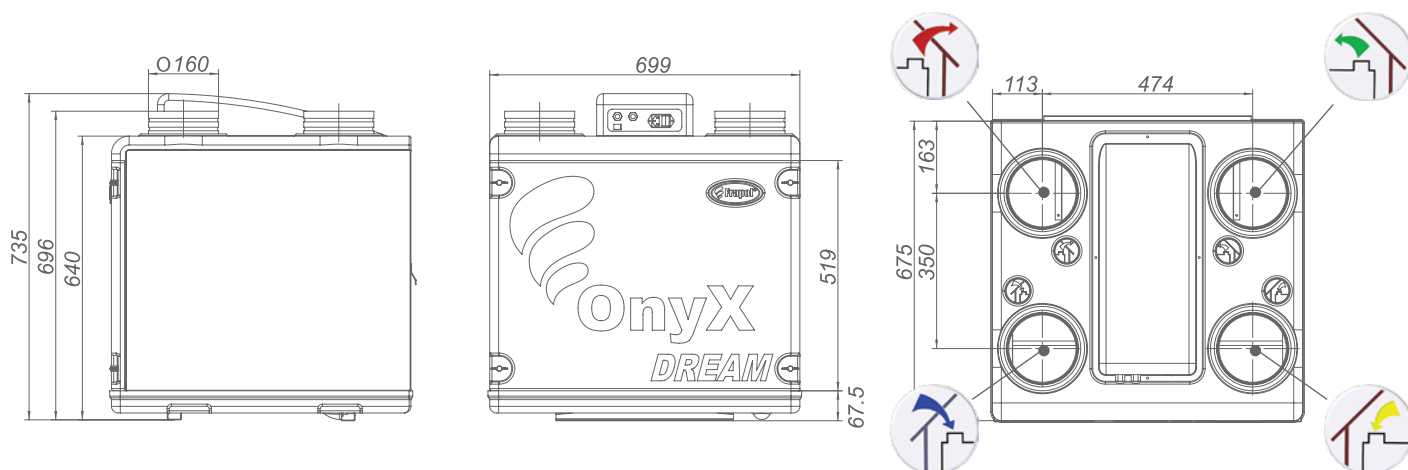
Внешние размеры вентиляционной установки Onyx Dream 400
